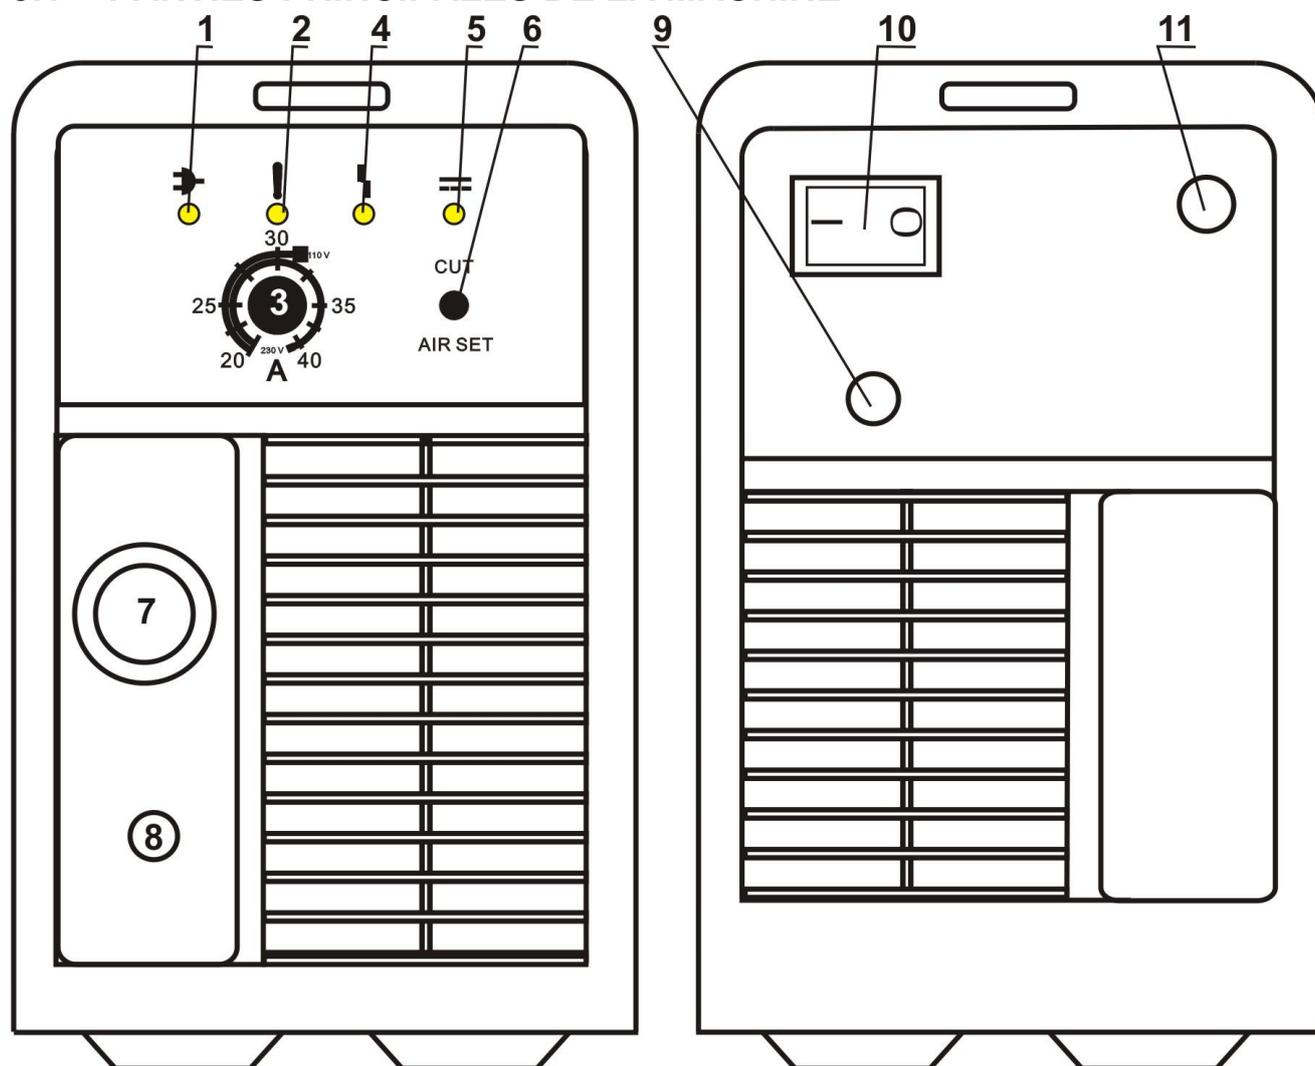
Parties principales de la machine, vue en face et vue d'arrière
